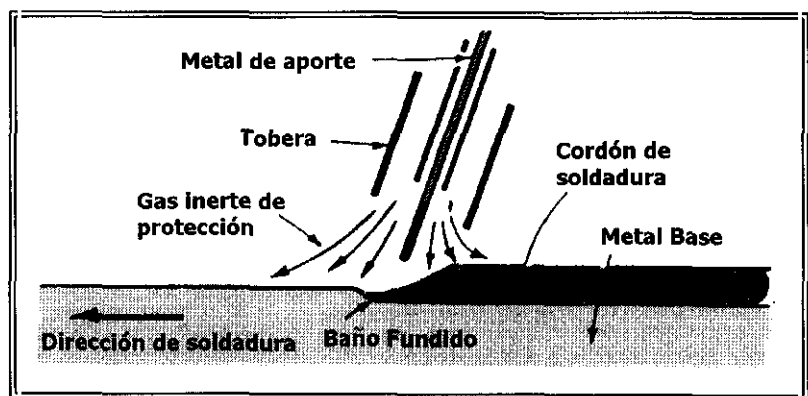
Esquema del proceso de soldadura MIG.
